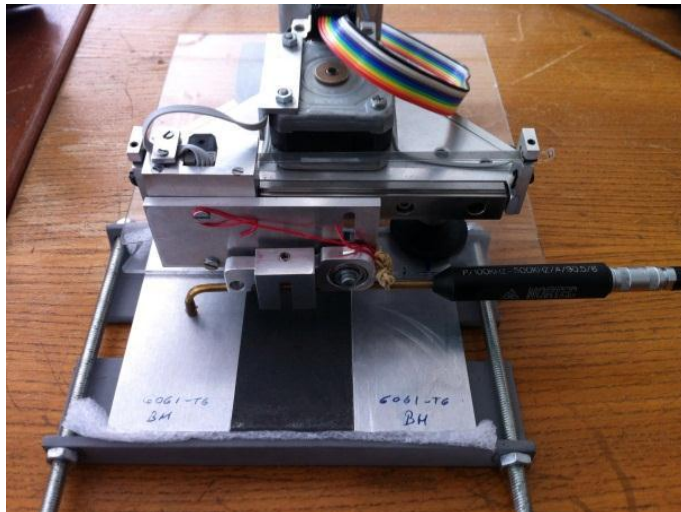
Junta bimetálica Al – Aço – Al, no acto de inspecção.
